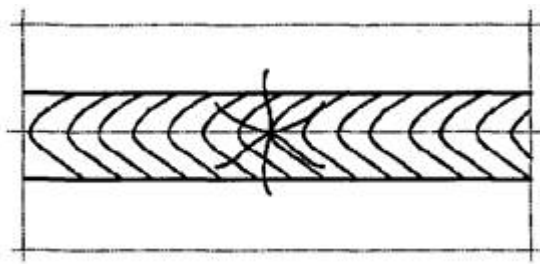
Радиальная трещина сварного соединения
